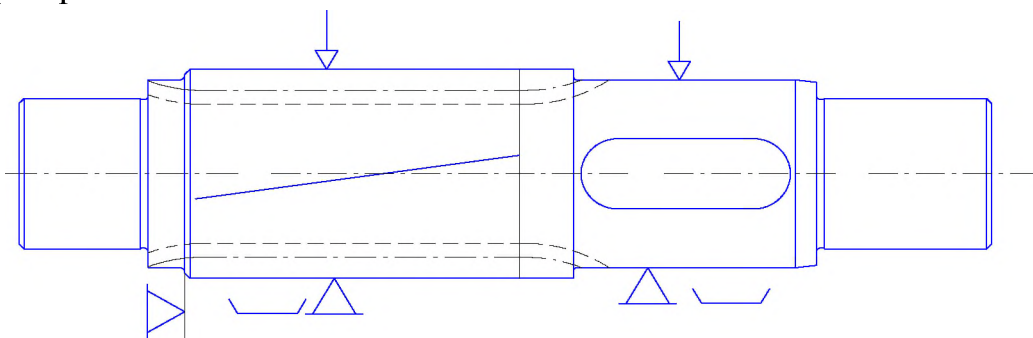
Установка вала на призмі з упором у торцеві
